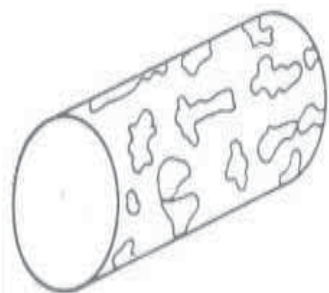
Внешний вид прутка с перетравленной поверхностью
